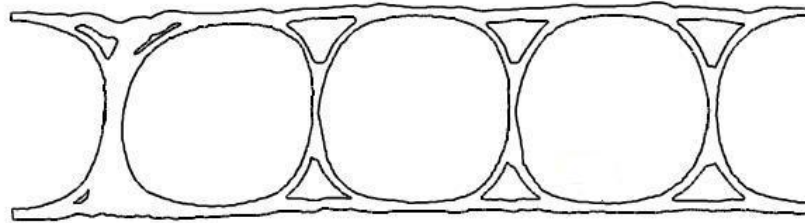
Korige Boru Profil Yüksekliği 55.15 mm [10]
